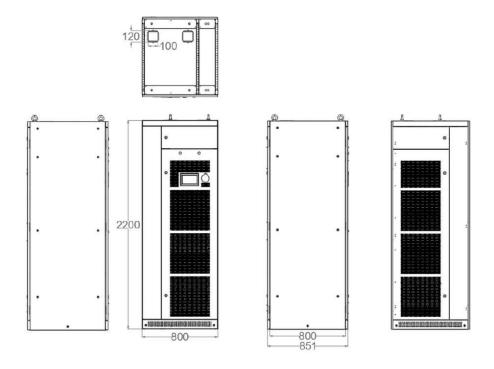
Внешние размеры стандартного шкафа 800*800*2200
